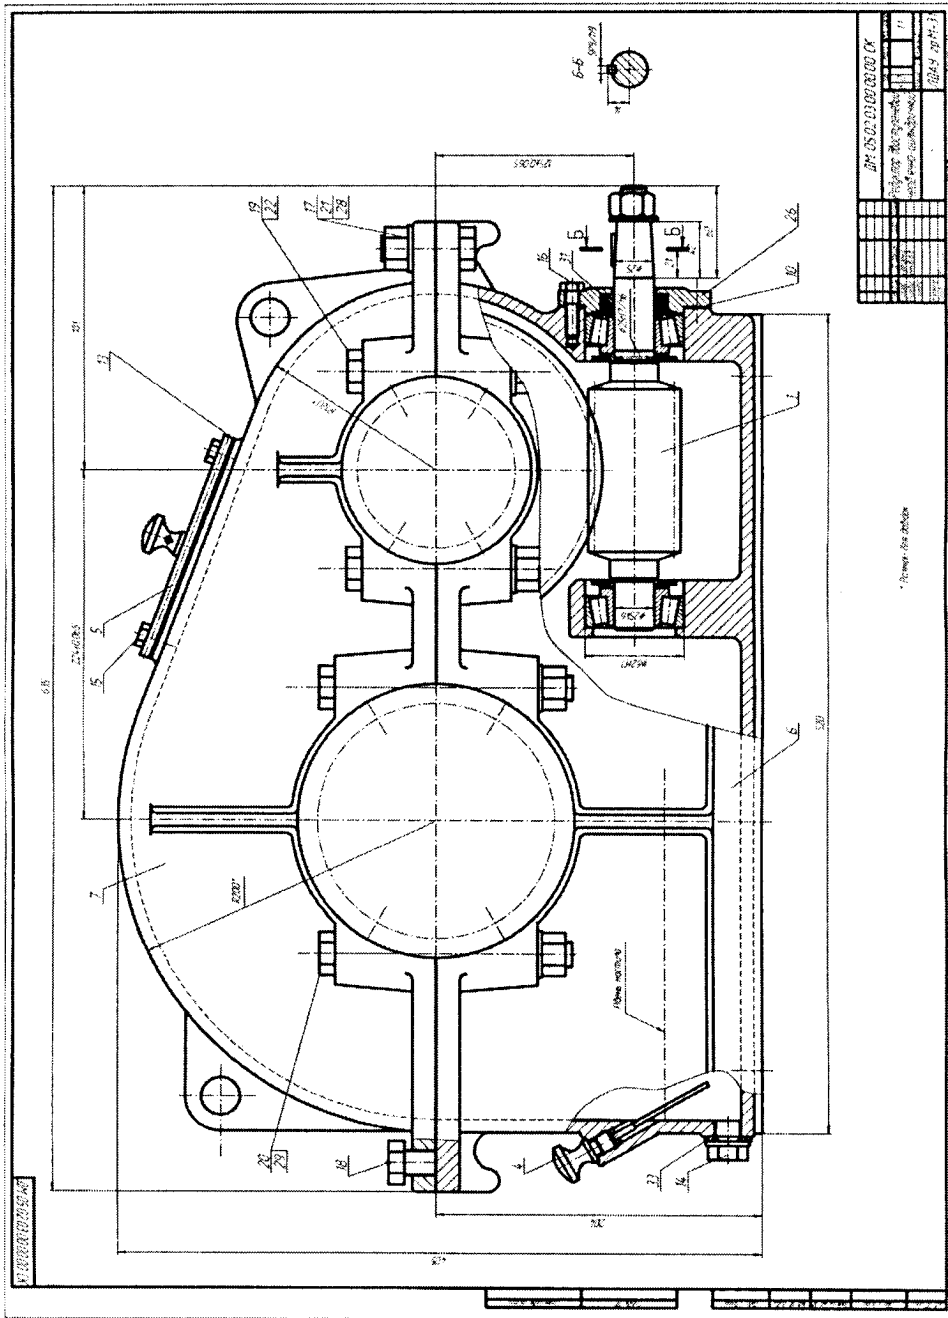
Черв'ячно-циліндричний редуктор (вигляд збоку)
